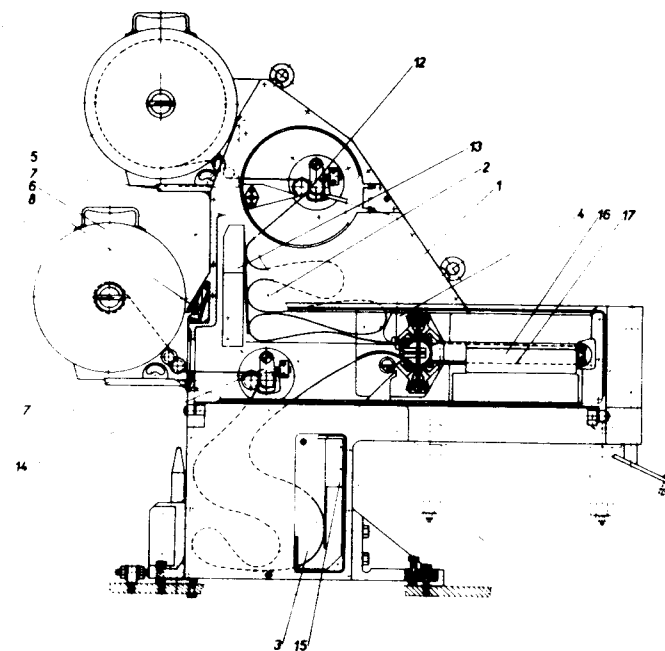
Общий вид фоторегистратора. 1 - корпус, 2 - питающий бункер, 3 - приемный бункер, 4 - лентопротяжный механизм, 5-6 - кассеты, 7 - направляющая, 8 - защелка, 12 - подающие ролики, 13 - контактный датчик питающего бункера, 14 - тормозные ролики, 15 - контактный датчик приемного бункера, 16 - фильмовый канал, 17 - столик.
